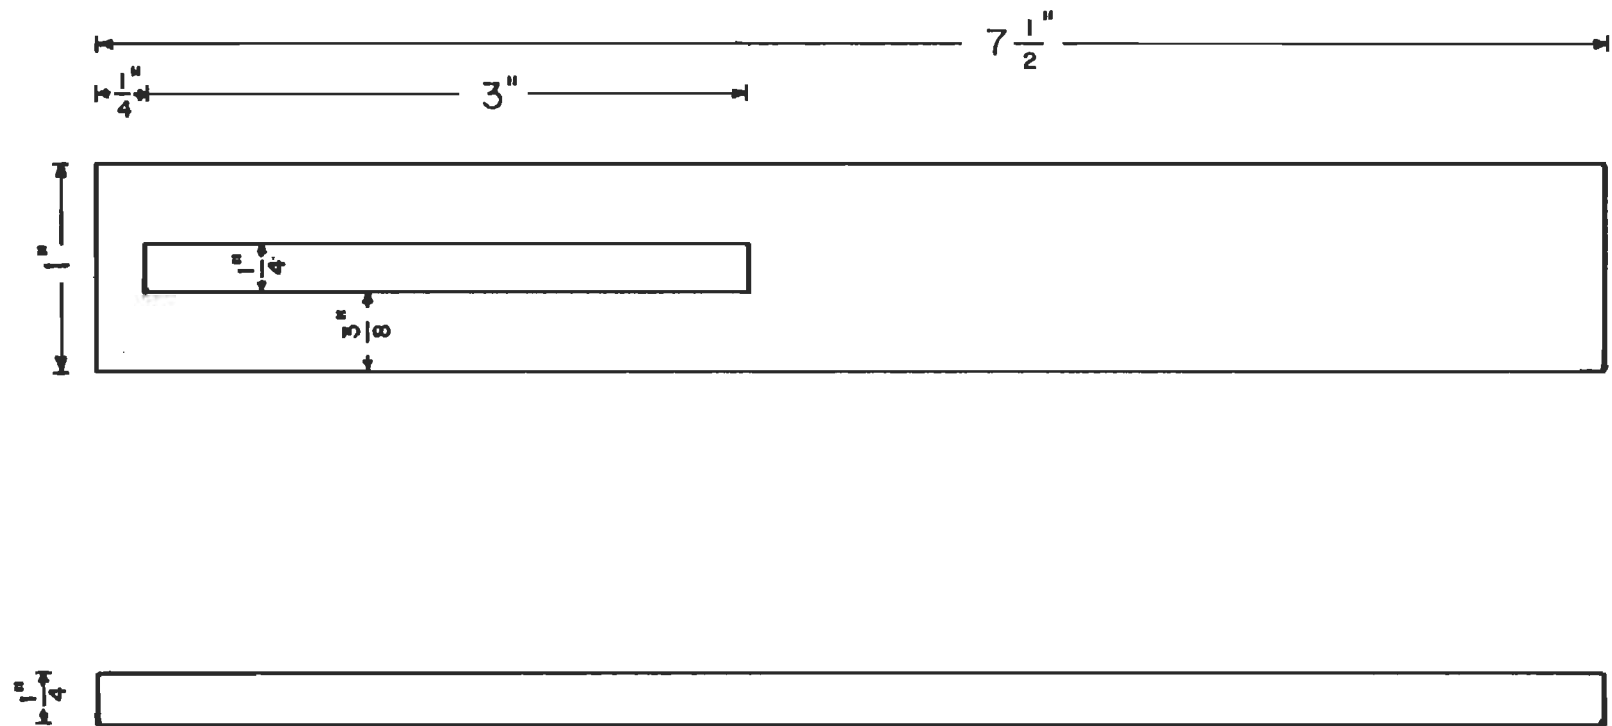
Plan détaillé de la section horizontale recevant la source ponctuelle.
